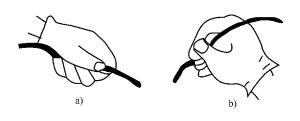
焊锡丝的拿法 a) 连续焊锡丝拿法 b) 断续焊锡丝拿法
